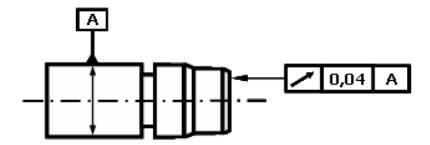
Indicação de tolerância de batida axial em desenho técnico
